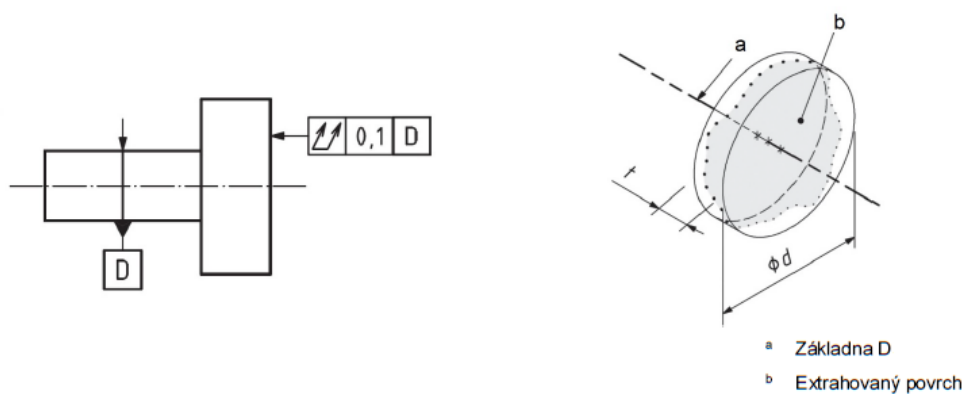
Indikace tolerance házení ve směru [14]
